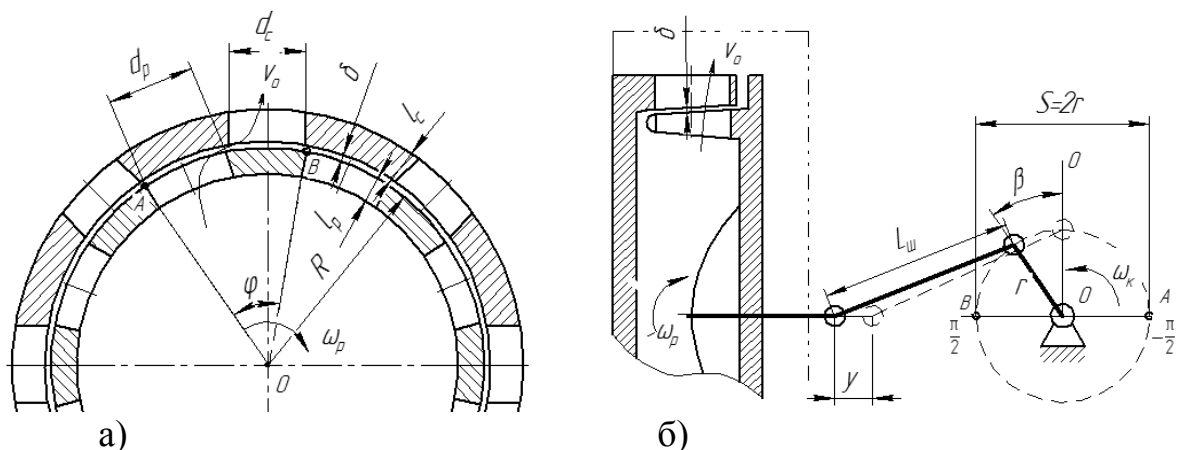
Рассчётная схема ПА з ВР: а) схема ротора и статора, б) схема привода вибрации ротора – кривошипного механизма.
